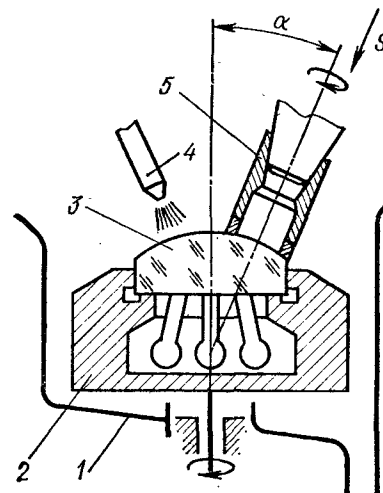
Шлифование единичных заготовок трубчатым алмазным инструментом
